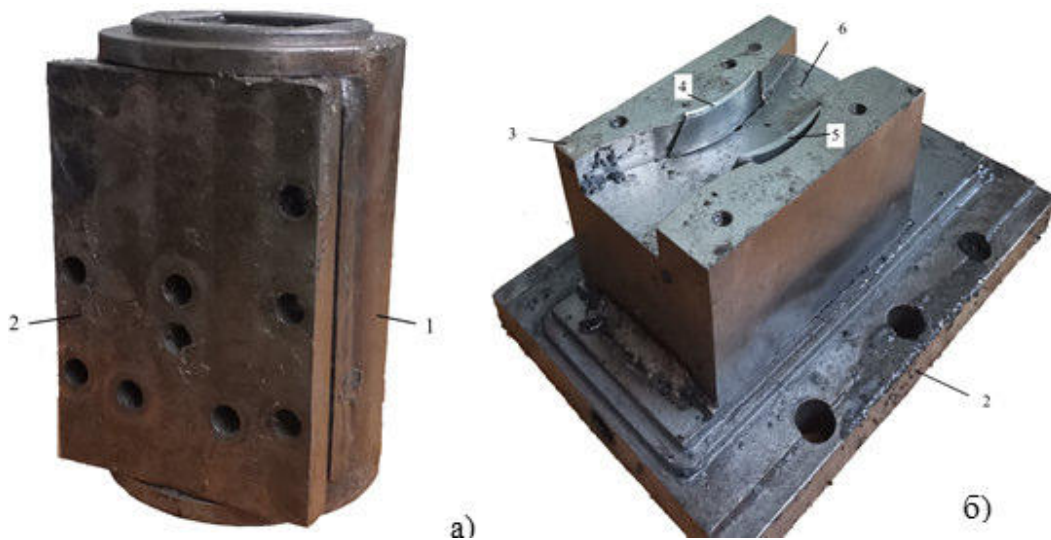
Приспособление – имитатор внутреннего канала литой заготовки: а) общий вид; б) съемная часть: 1 - корпус; 2 - плата; 3 - основание; 4 - выгнутый образец; 5 - вогнутый образец; 6 - криволинейный канал
